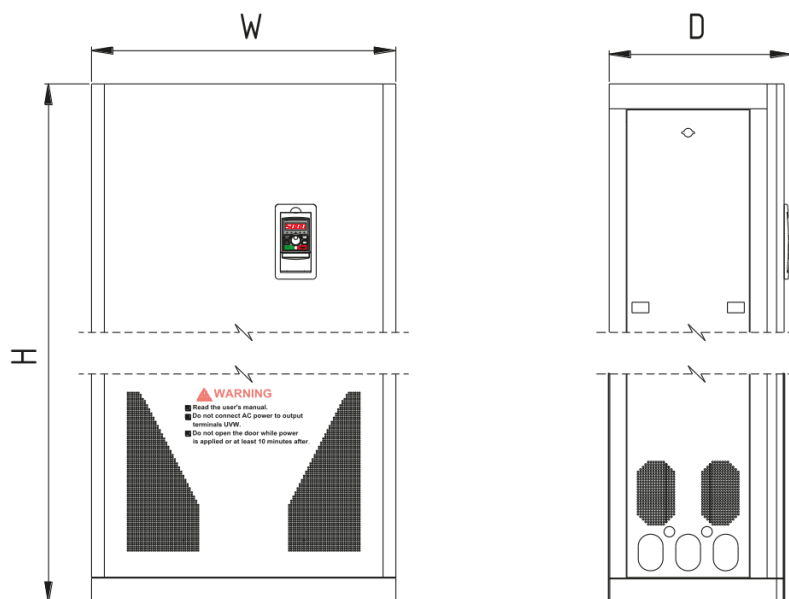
(Модель С) Внешний вид и размеры ПЧ
